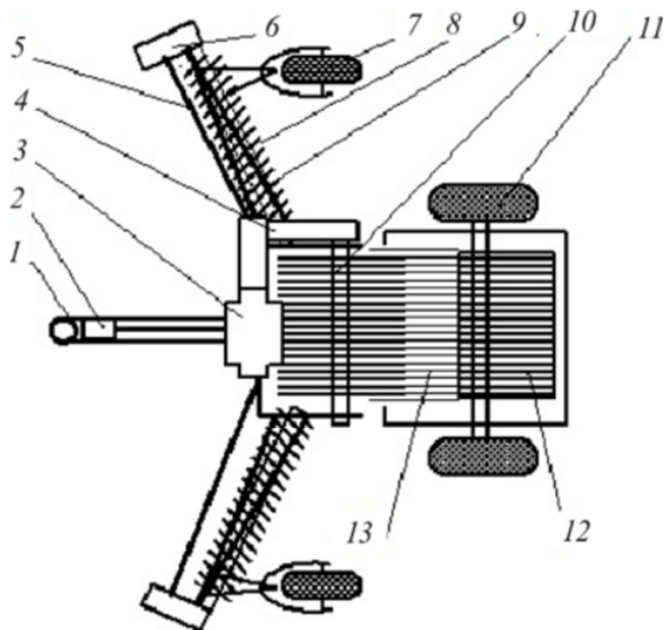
Схема валкователя-подборщика камней: 1 — прицепное дышло; 2 — карданный вал; 3 — раздаточный редуктор; 4 — привод подбирающего ротора; 5 — карданный вал привода валкующих роторов; 6 — редуктор привода валкующих роторов; 7 —
